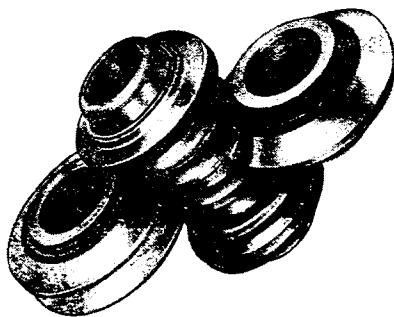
Схема профильного прикатывания нитки глобоидного червяка
